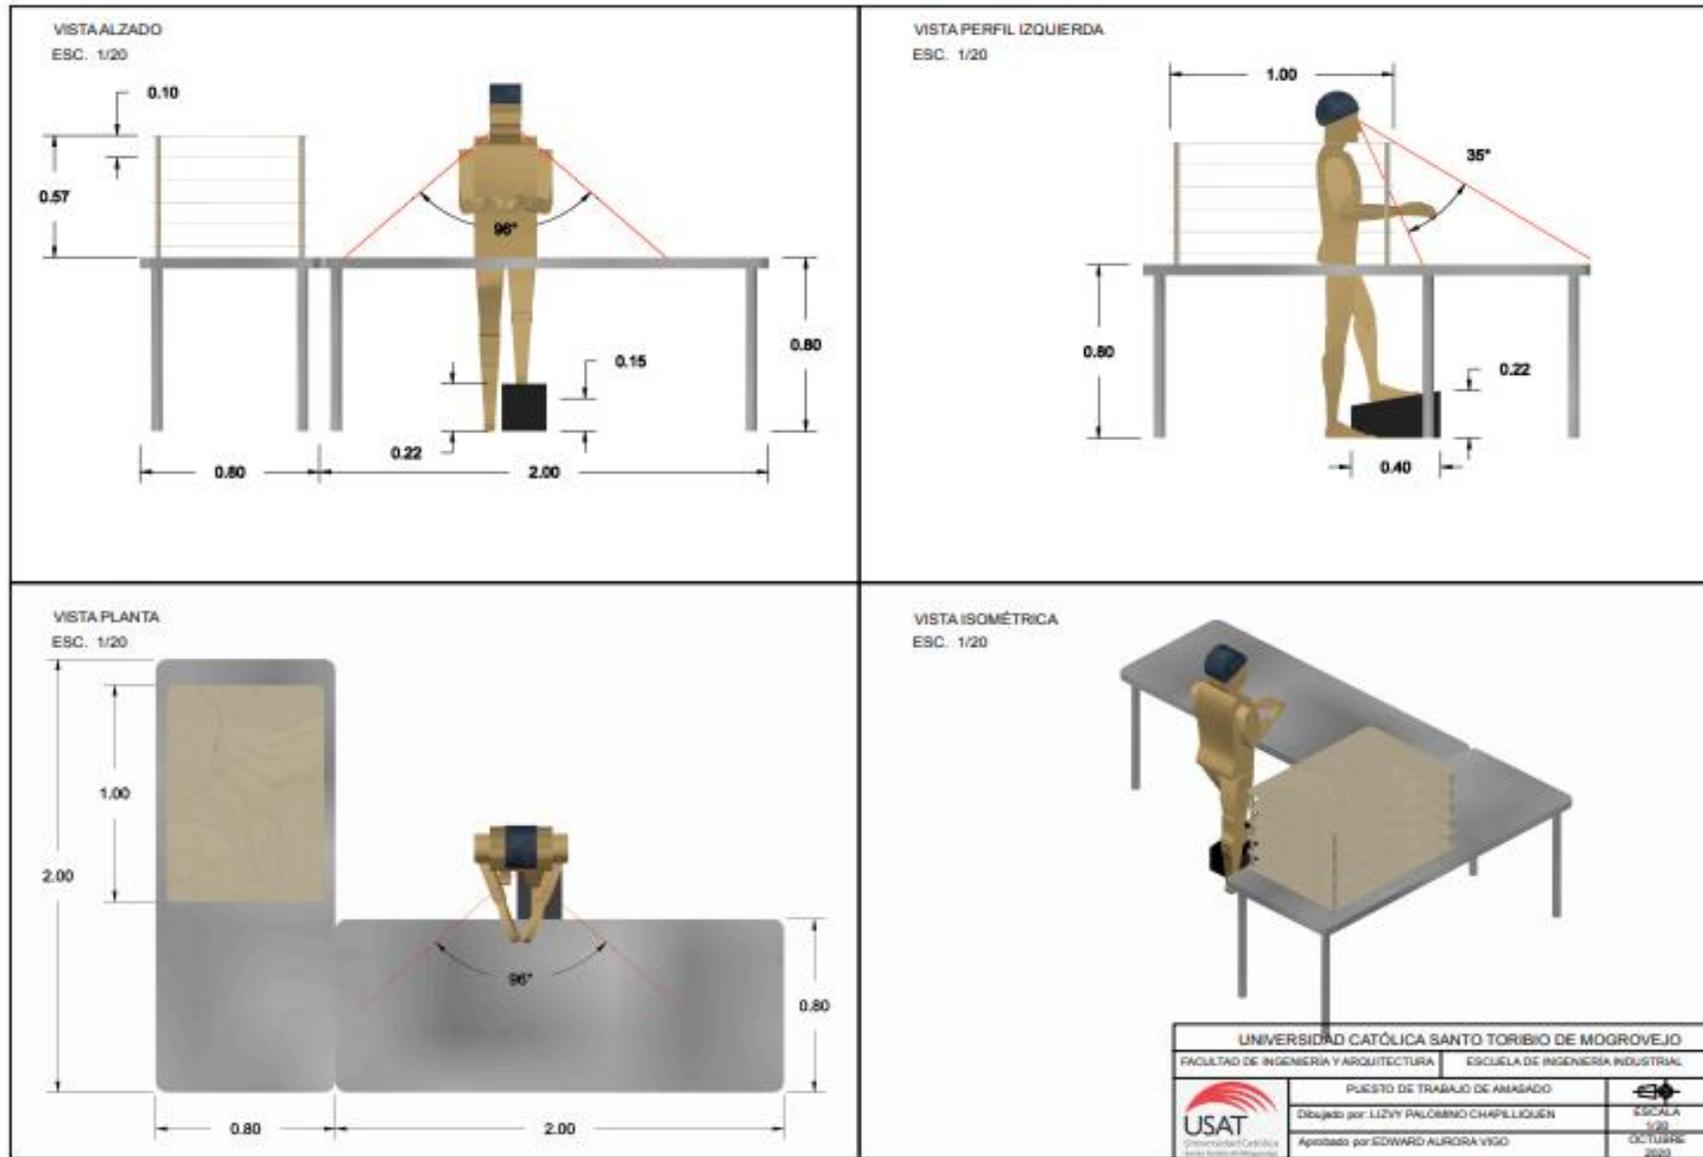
Vistas del puesto de trabajo mejorado de amasado
